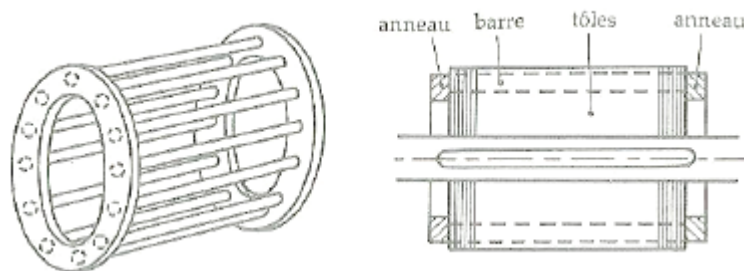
Cage (à droite) et rotor à cage (à gauche) [SEG-96].
